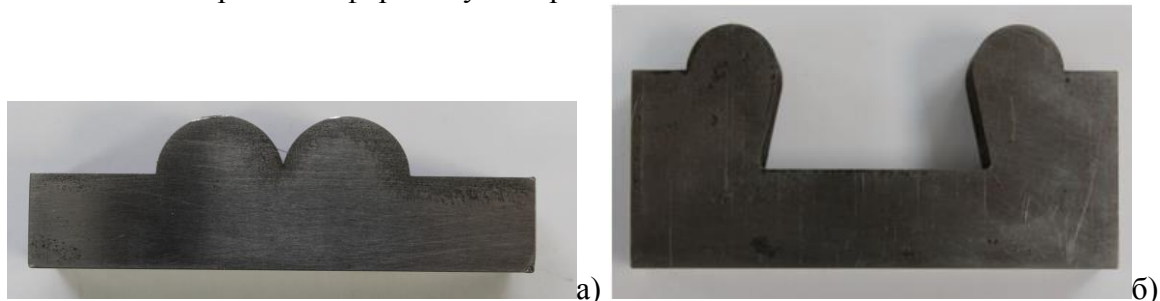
Матрица для: а) подгибки кромок, б) предварительной формовки заготовки
